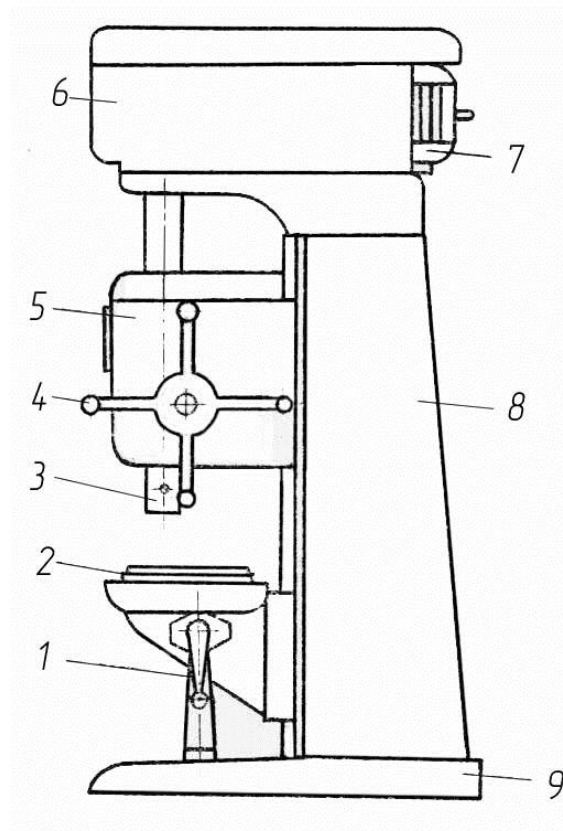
Схема вертикально-сверлильного станка модели 2A135
